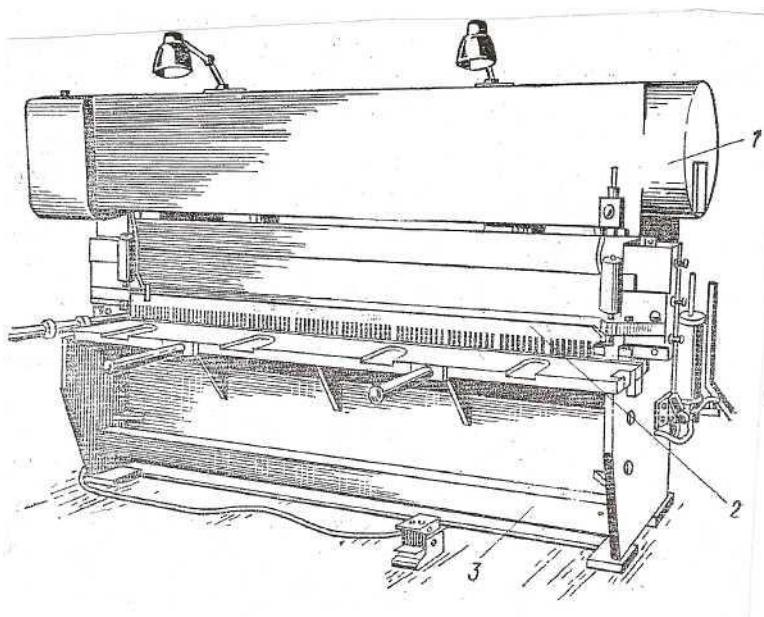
Механизм для отрезки листового металла СТД-9А.
